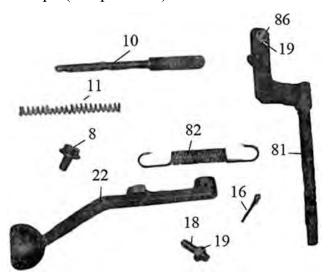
Детали механизма ручного спуска: $8,\ 18,\ 86$ – винты; 10 – толкатель; 11 – пружина; 16 – шплинт; 19 – гайка; 22 – рукоятка; 81 – рычаг с осью; 82 – пружина
